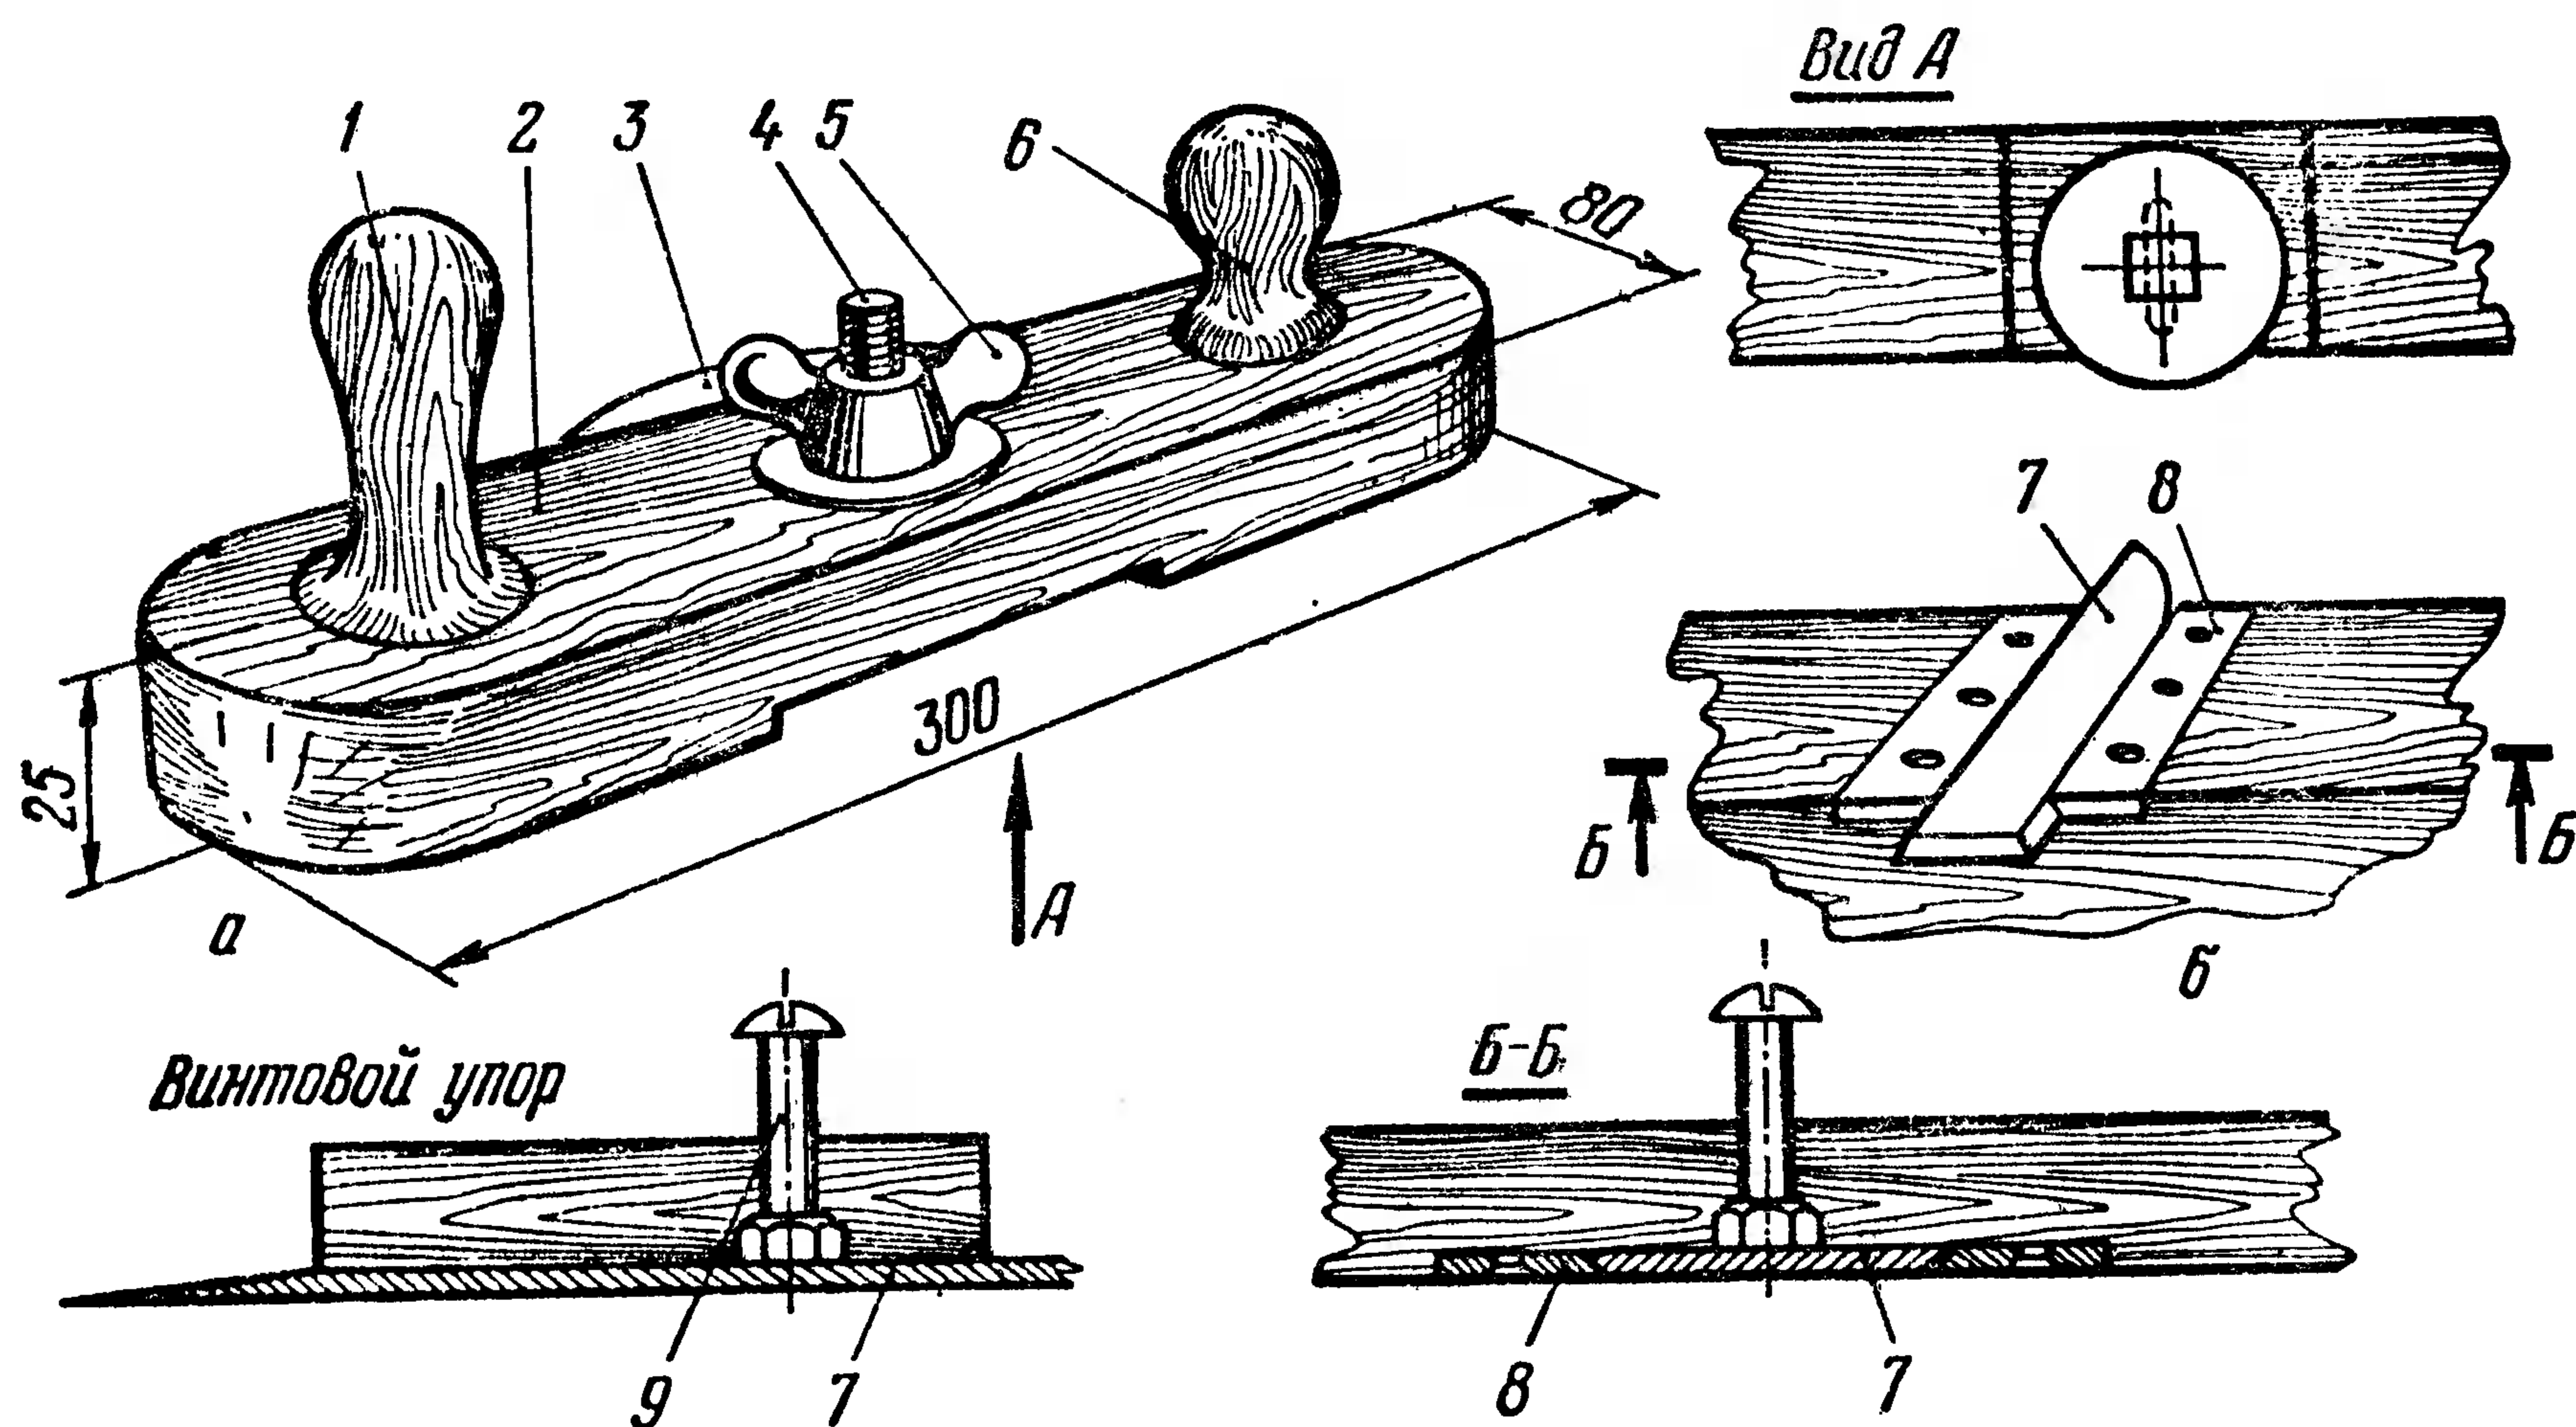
Крепление ножа в колодке: а — дискового; б — универсального; 1 — упорная ручка; 2 — колодка; 3 — нож дисковый; 4 — винт; 5 — гайка; 6 — нажимная ручка; 7 — лезвие переплетного (универсального) ножа; 8 — крепежные пластинки; 9 — винтовой упор.
